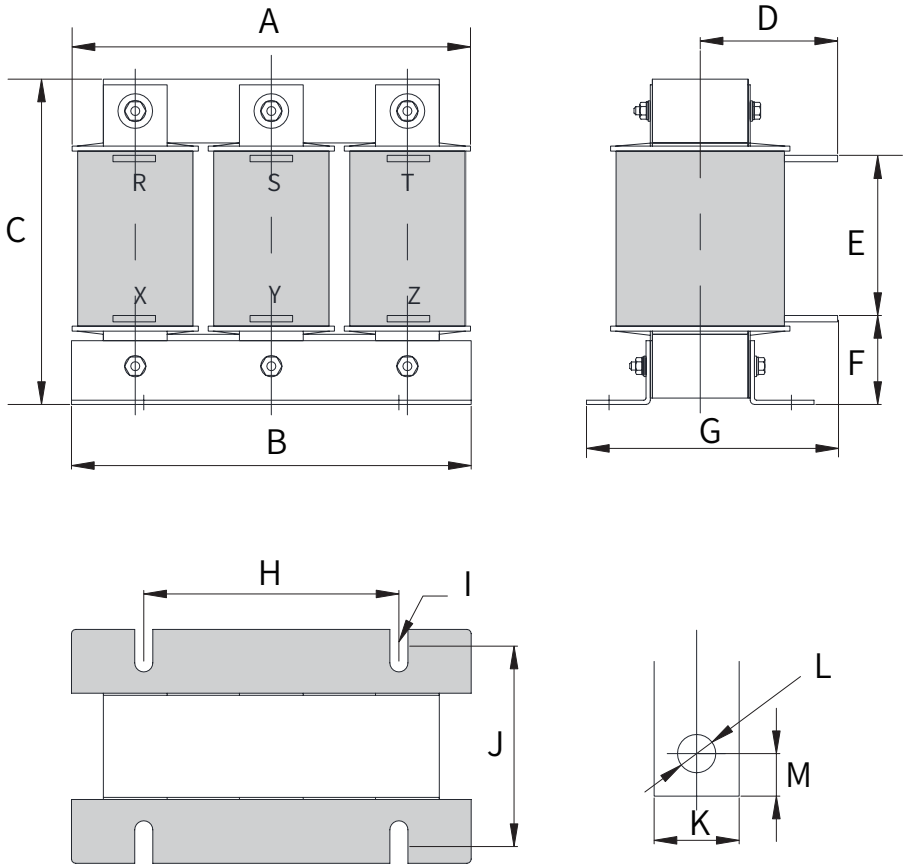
Размеры входного реактора переменного тока 90/120 А
